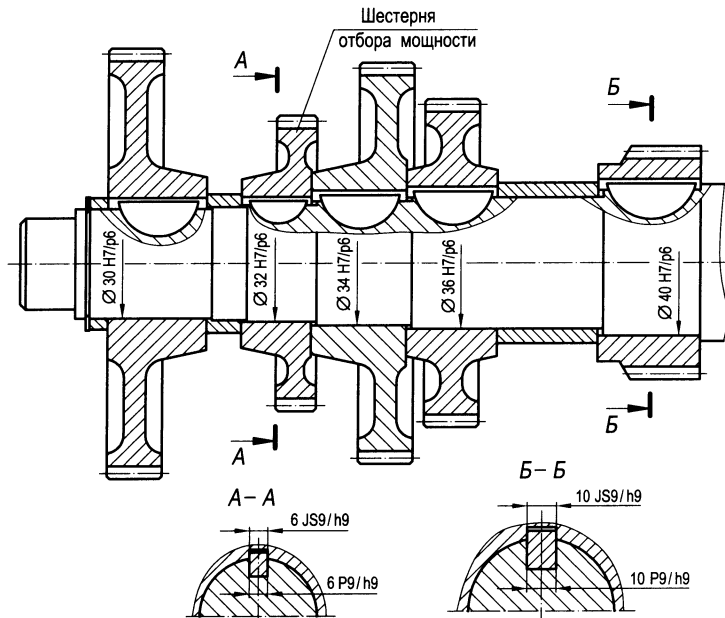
Соединение зубчатых колес с валом коробки передач сегментными шпонками
